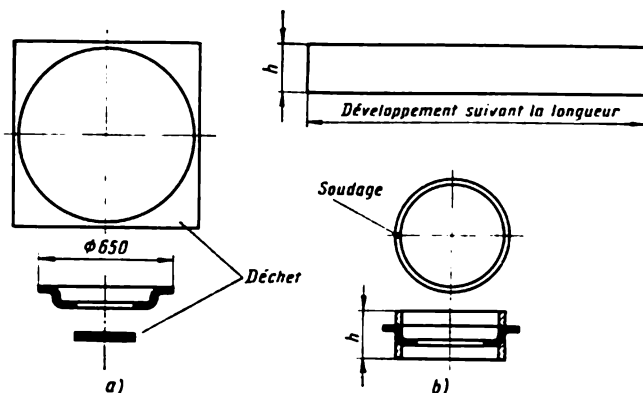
Utilisation du soudage permettant de faire économie de métal: a — pièce exécutée à partir d'une tôle (déchet important); b — pièce exécutée par soudage (sans déchet)
